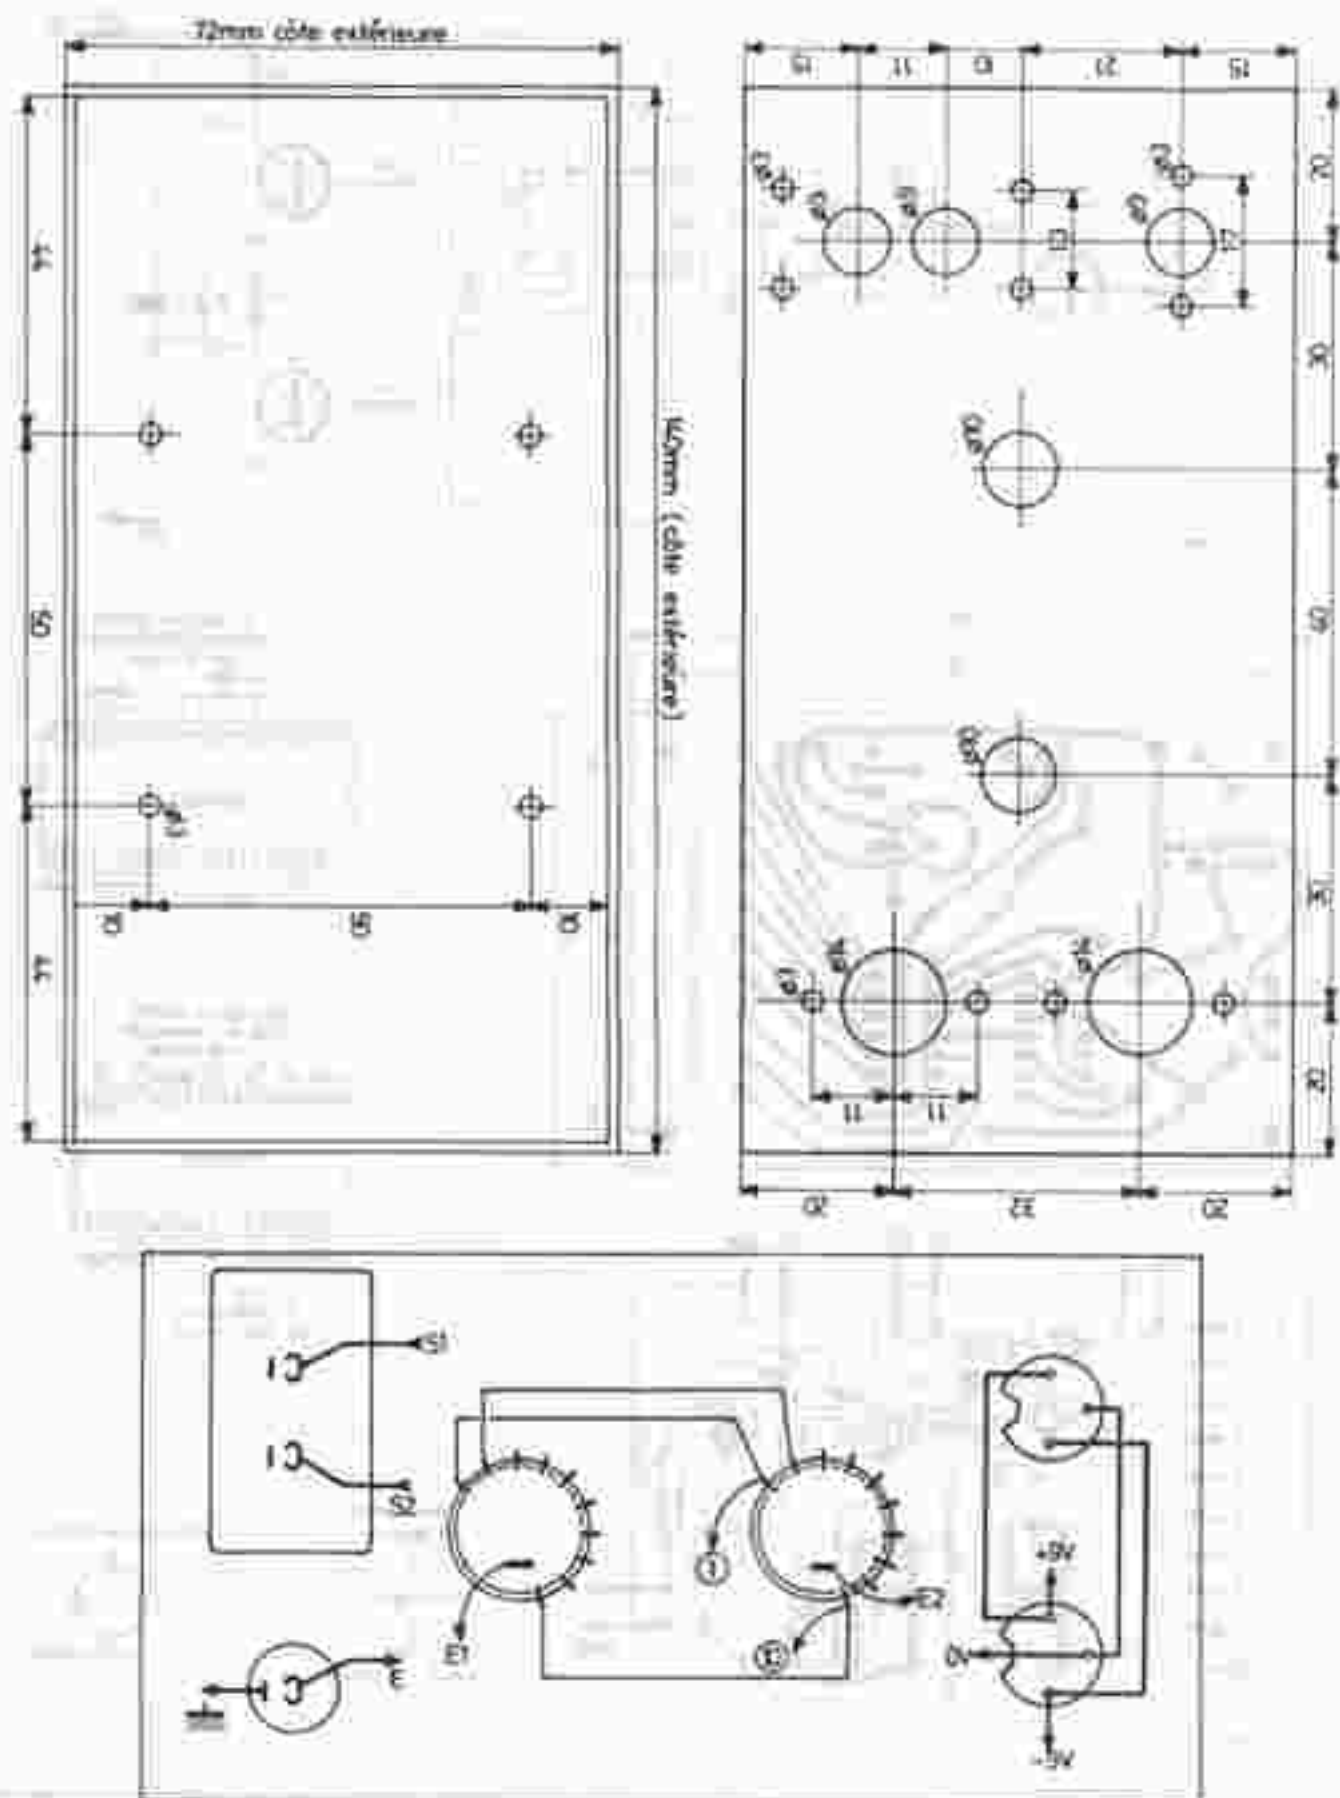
à 14. – Plan de perçage du fond du boîtier, de la face avant et plan de câblage du module en question
